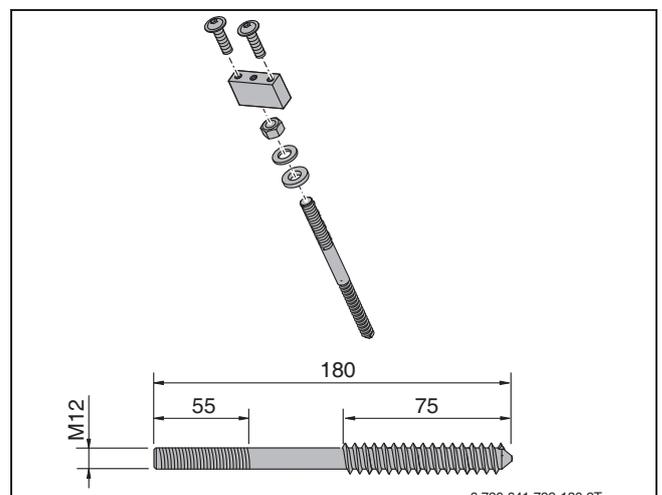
Vite prigioniera per il collegamento da tetto di piastre ondulate o lamiera CKN1.0 e SKS4.0 (misure in mm)
